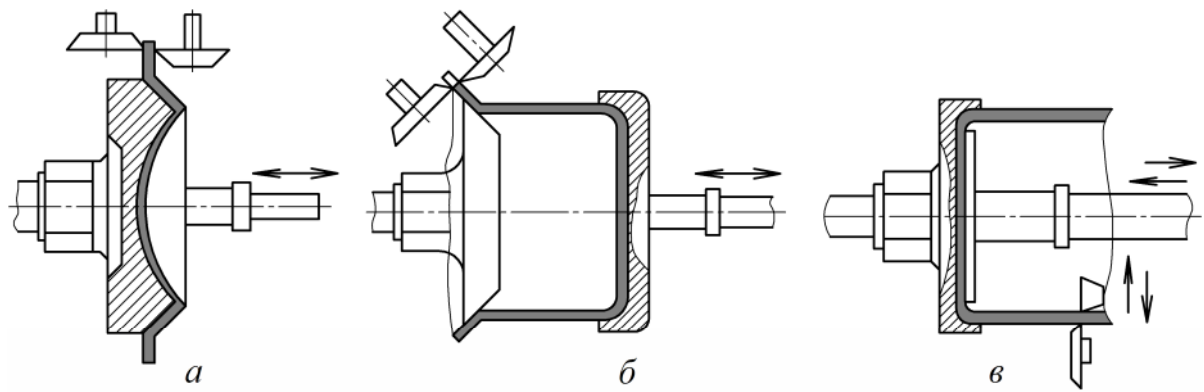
Схеми розташування ножів під час обрізання напівфабрикатів різної форми:
